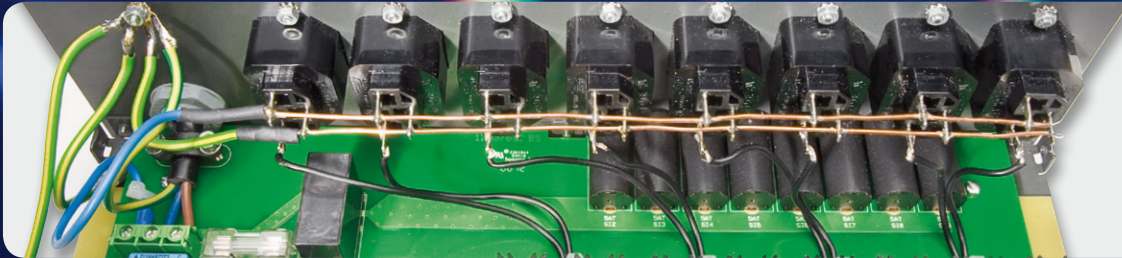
Die komplett verkabelten Kaltgerätebuchsen.
